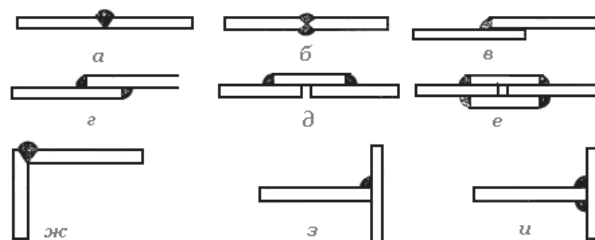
Основные типы сварочных соединений: а – стыковое с односторонним скосом кромок, б – стыковое с двусторонним скосом кромок, в – нахлесточное с одним швом, г – нахлесточное с двумя швами, д – стыковое с накладкой, е – стыковое с двумя накладками, ж – угловое, з – тавровое с одним швом, и – тавровое с двумя швами
